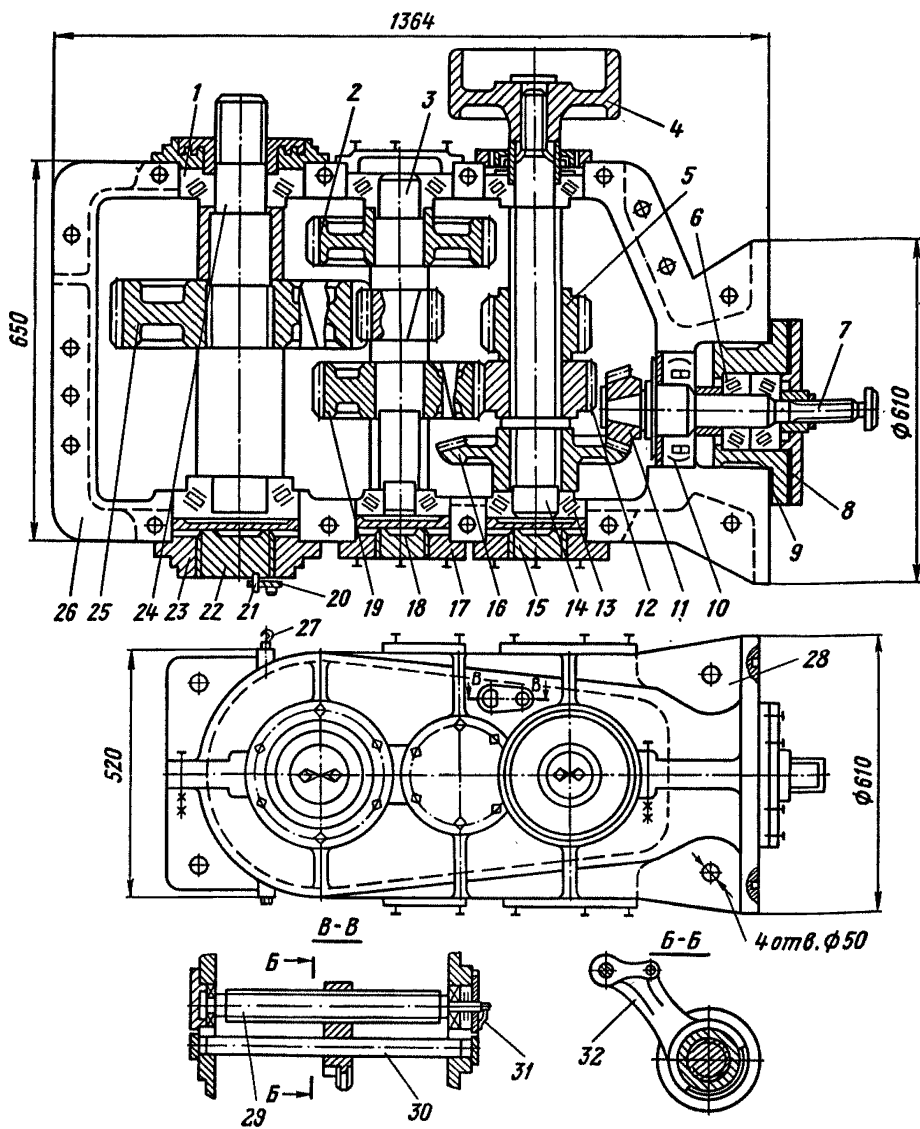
Цилиндро-конический редуктор конвейера 2J180
